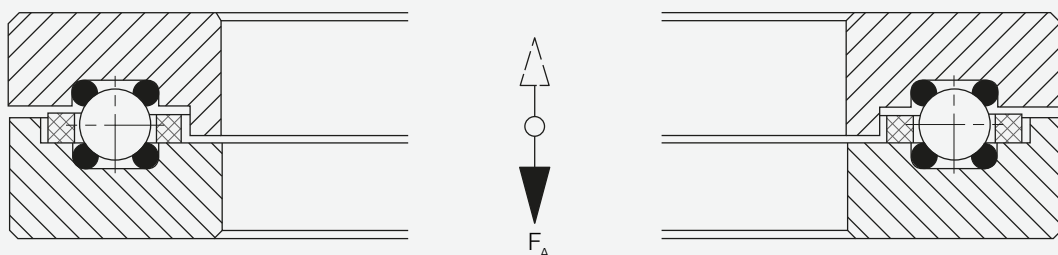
Franke Längslager für die Aufnahme von einseitig wirkenden Axialkräften.
